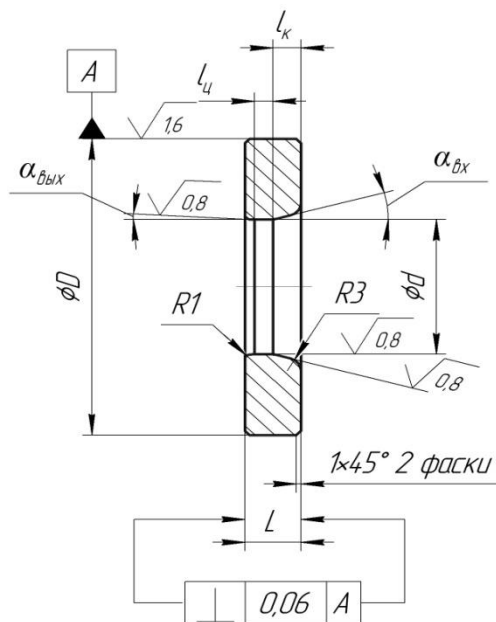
Протяжное кольцо калибровочного пресса
